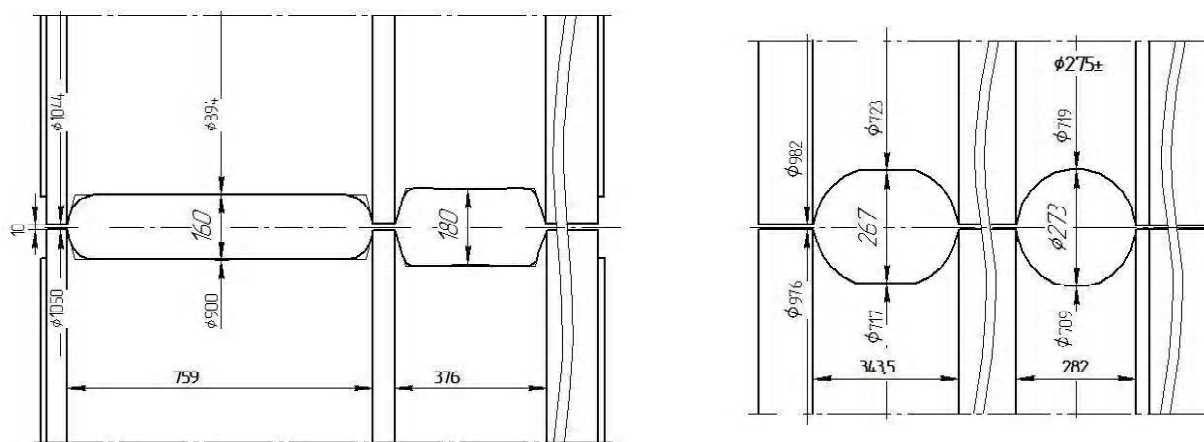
Калибровка валков обжимной (а) и заготовочной (б) клетки
